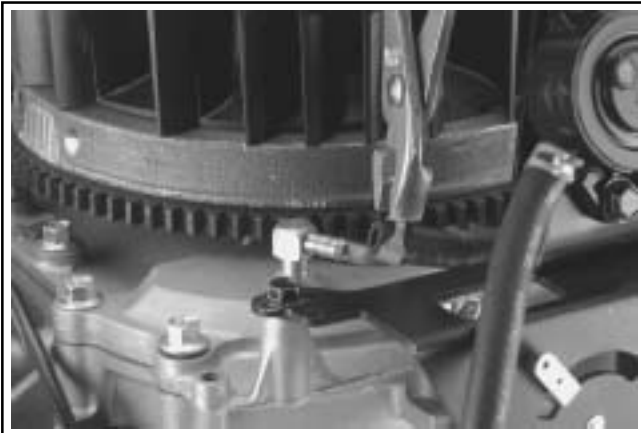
Desconexión de la tubería de combustible del carburador.
